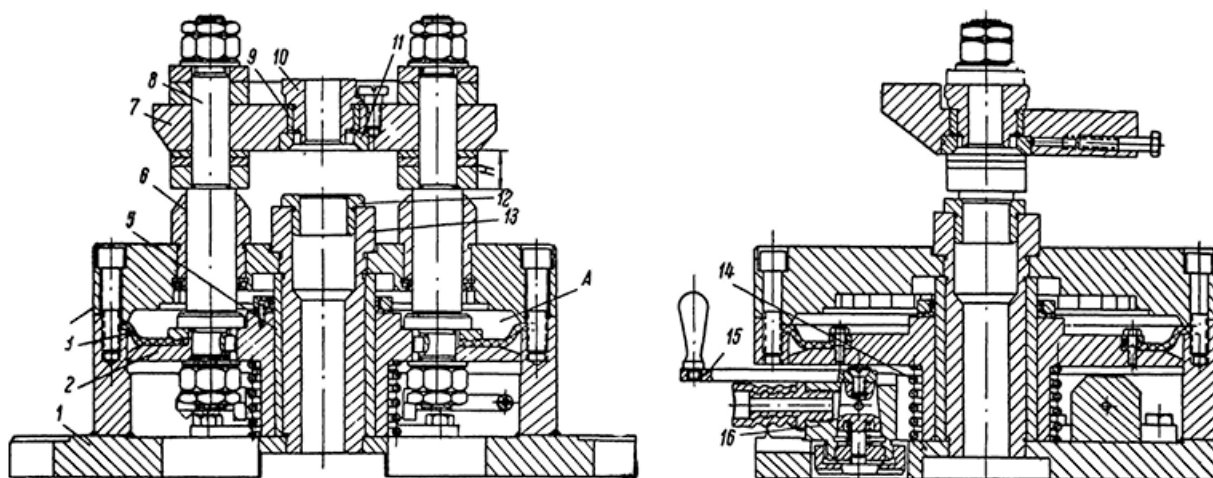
Скальчастий порталний кондуктор спрощеної конструкції
